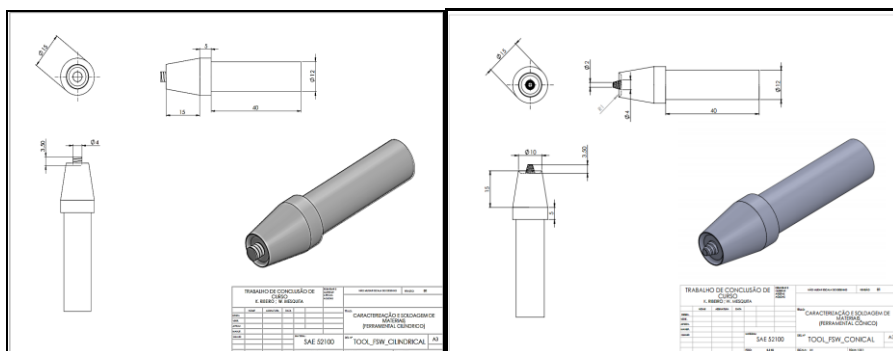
Desenho do ferramental com ponta cilíndrica (à esquerda) e cônica (à direita) fabricado em SAE 52100
